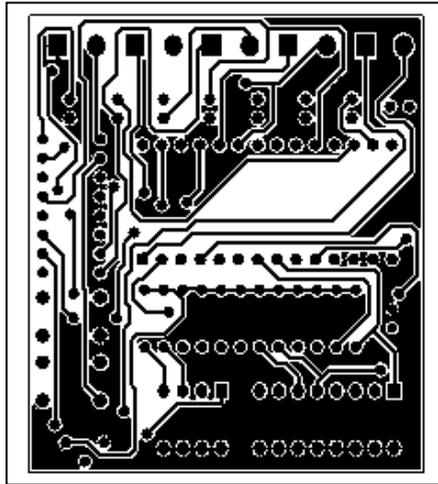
b. Cara Posterior del PCB de la Tarjeta Universal del ISD
